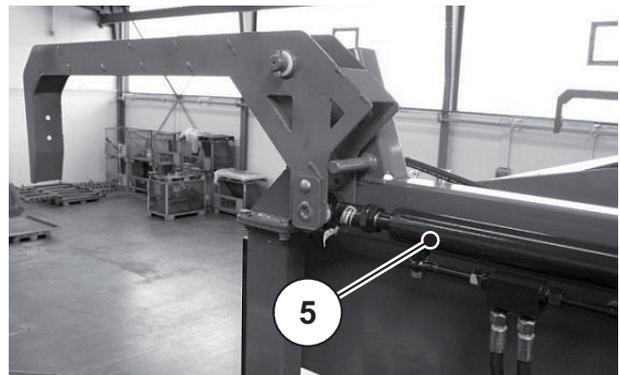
Гидроцилиндр транспортировочного крепления
